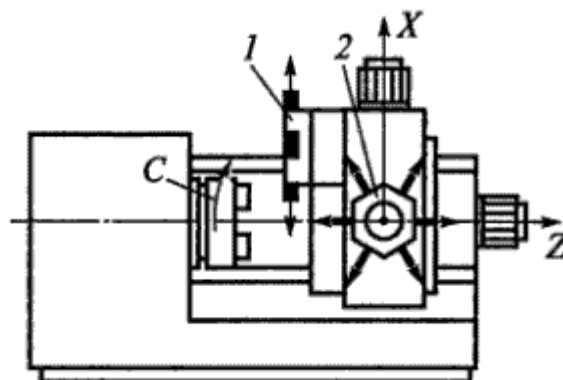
Токарный станок с ЧПУ (1,2 – револьверные головки)
